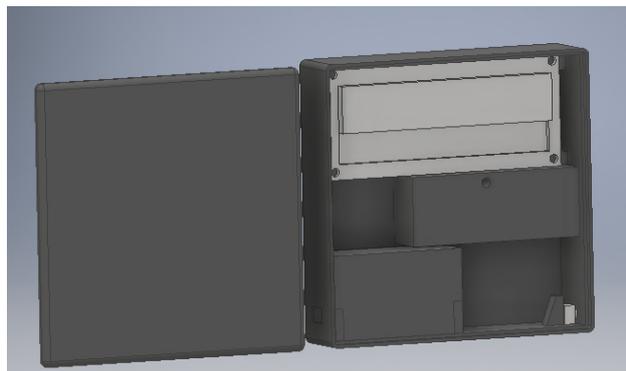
Трёхмерная модель корпуса с размещёнными деталями
